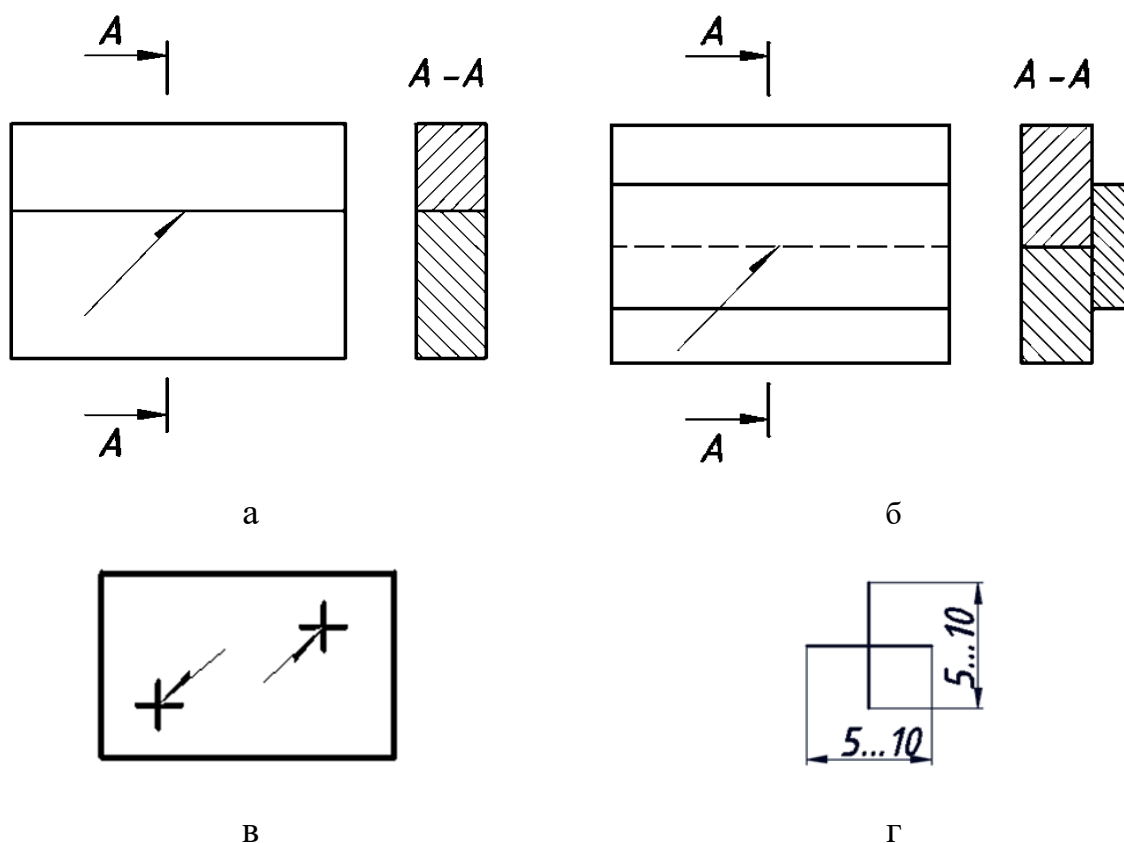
Образец изображения швов сварных соединений.
